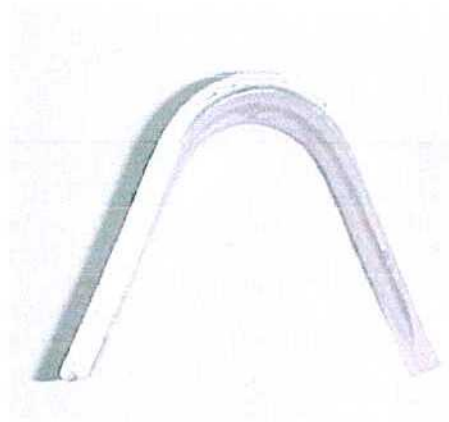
Soldadura Al-Al. Ensayo de plegado.
